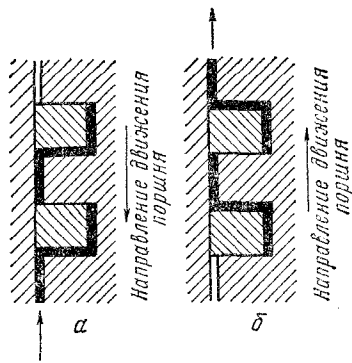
Схема насосного действия компрессионных колец: а — поршень движется вниз; б — поршень движется вверх.
